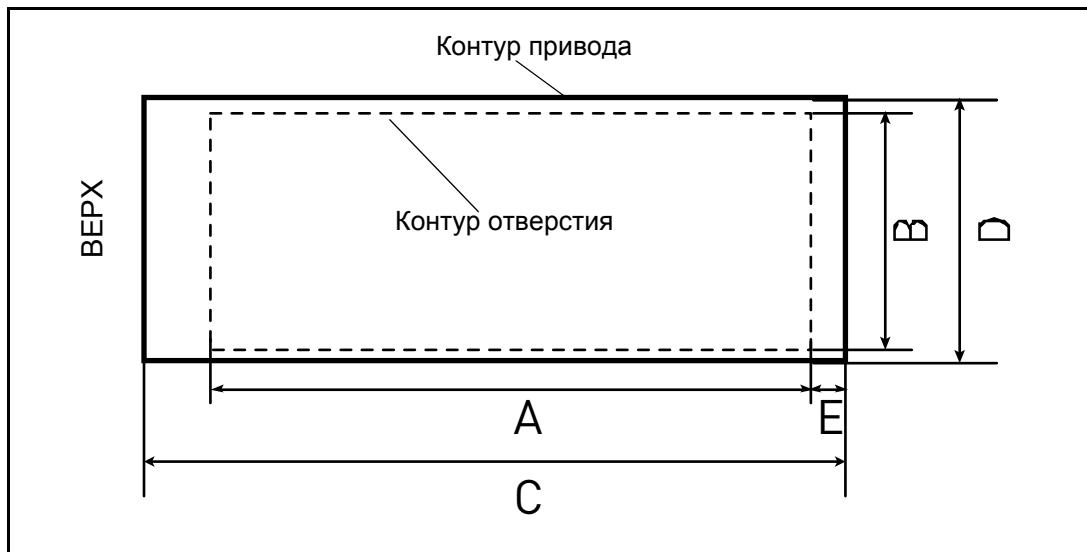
Размеры выреза для утопленного монтажа приводов типоразмеров MR7–MR9
